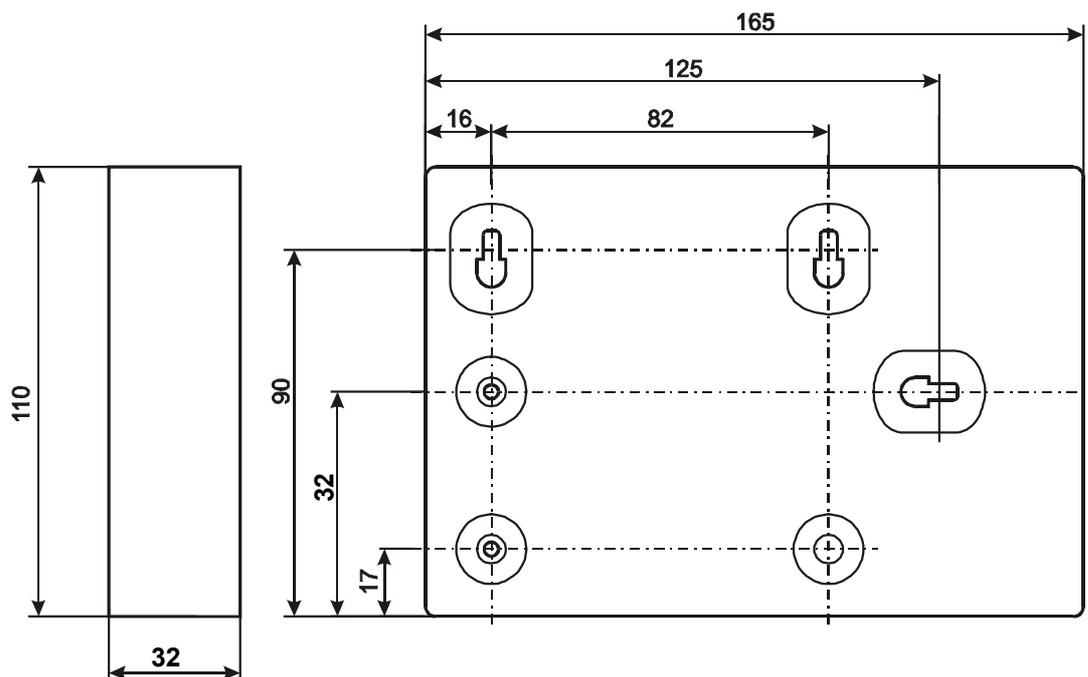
Внешний вид и габаритные размеры ПИ-01 в исп. IP 20
